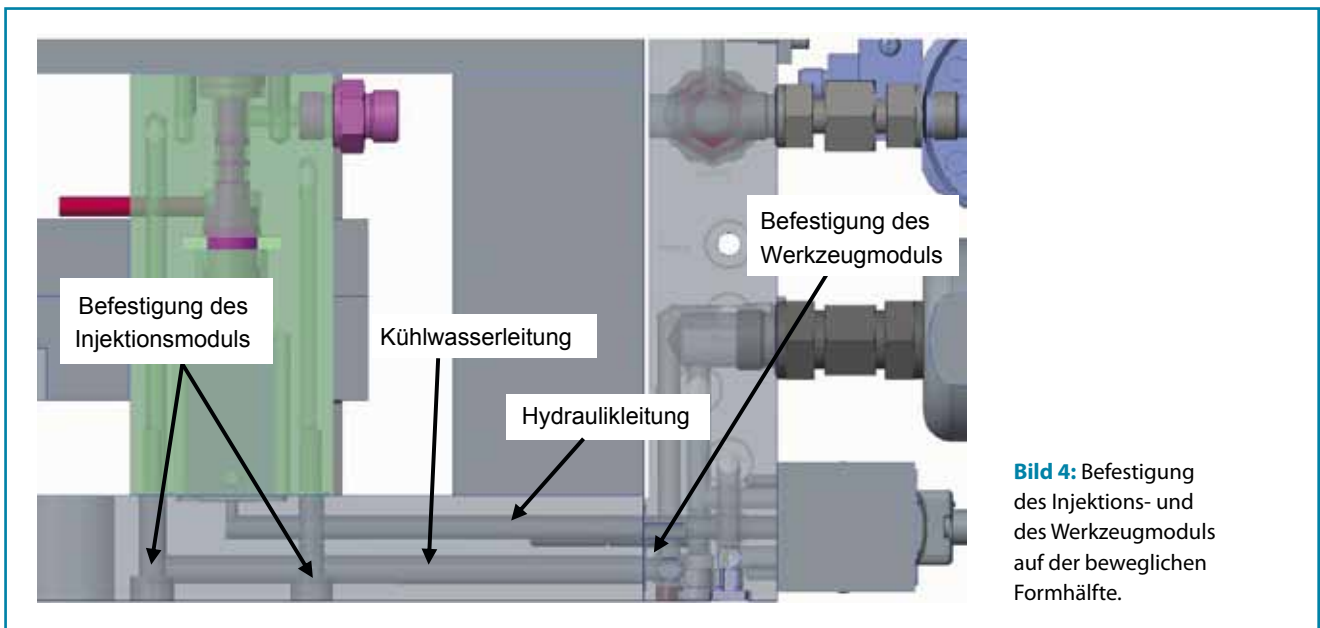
Befestigung des Injektions- und des Werkzeugmoduls auf der beweglichen Formhälfte.
